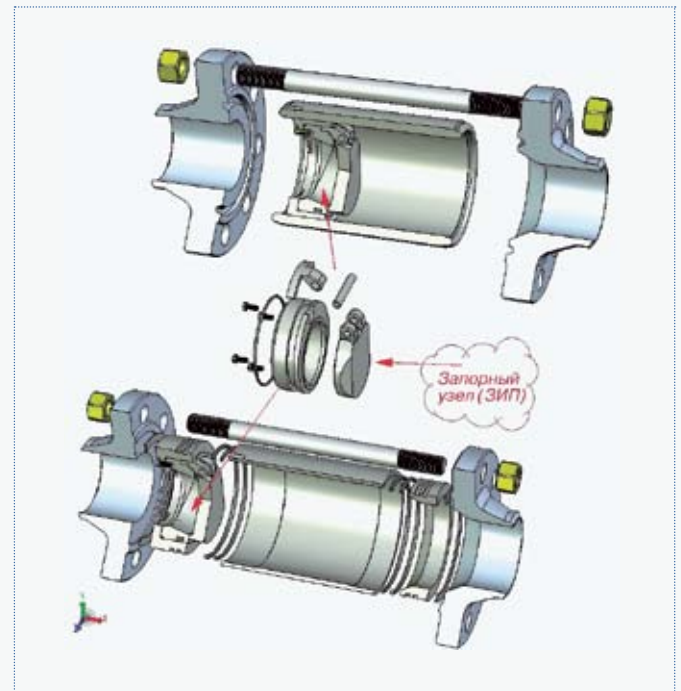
Запорный узел (ЗИП) затвора 19с11нж
